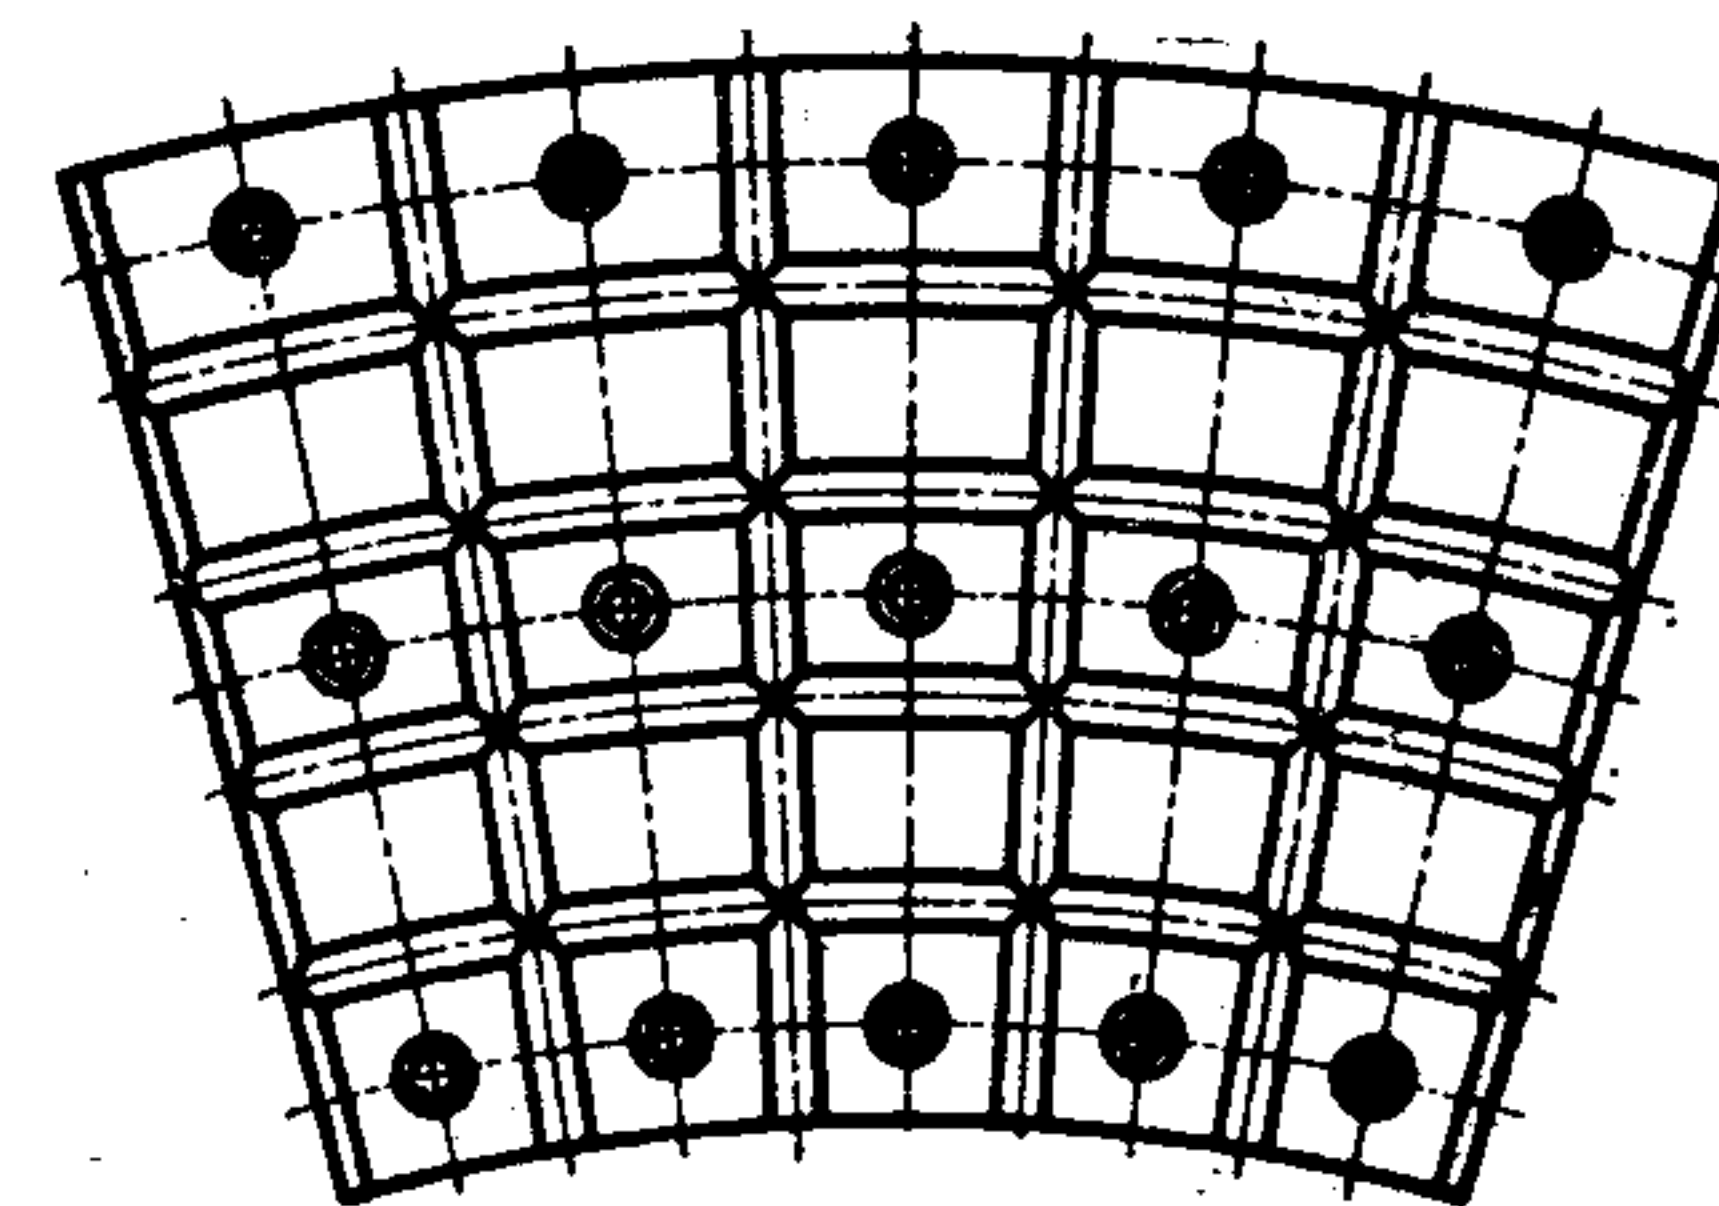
Схема расположения смазочных канавок в направляющей карусельного станка
